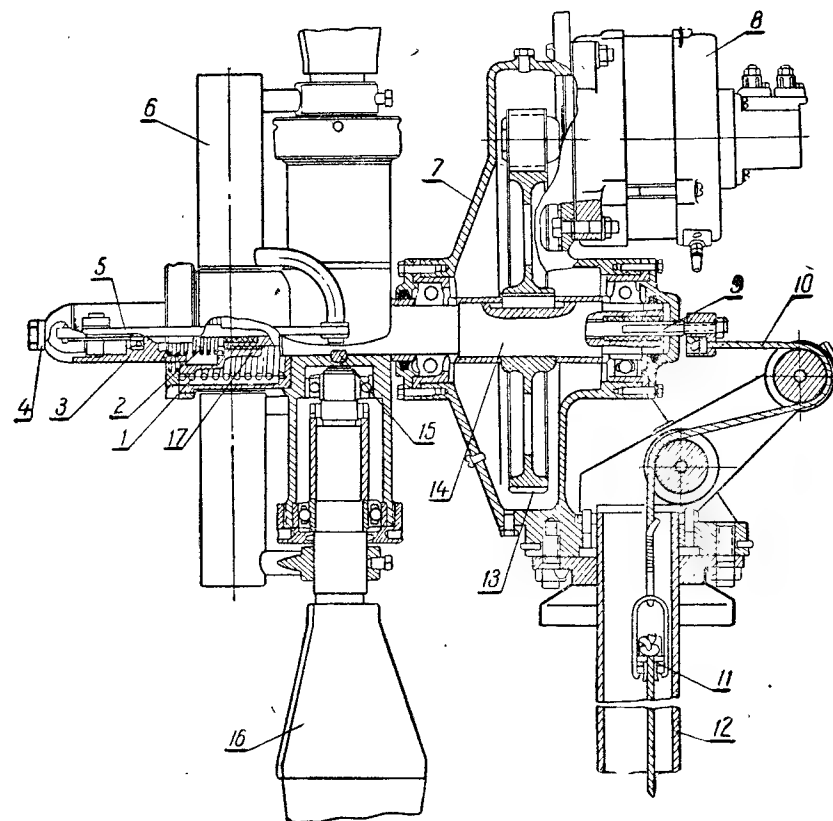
Головка агрегата Д-4 ВИЭСХ:
